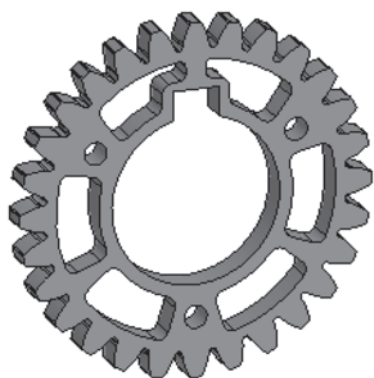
3D-модель листовой выкройки цилиндрической прямозубой шестерни
